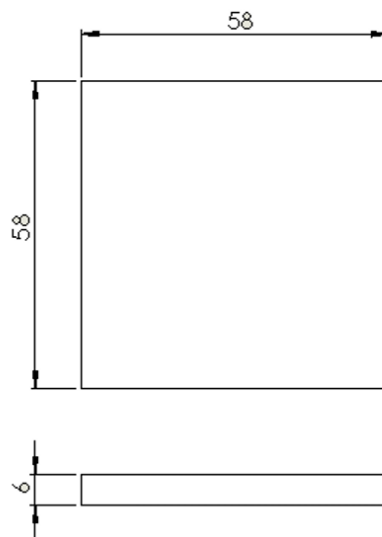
Dimensiones de la Probeta para el ensayo de Impacto [5].
